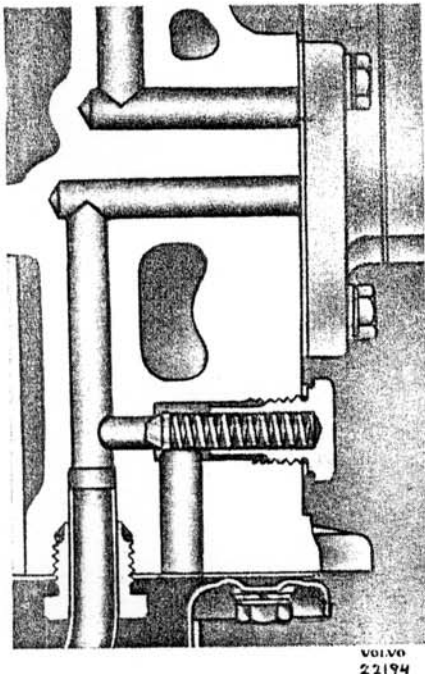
Ölüberdruckventil, D 47, an der linken Seite des Motors leicht zugänglich. Es besteht aus einem Ventilkegel sowie einer Feder, welche durch eine Schraube in ihrer Lage gehalten wird.
